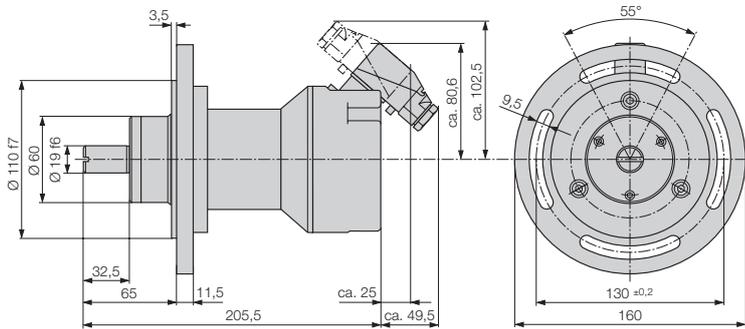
KINAX WT 707 mit Zusatzgetriebe, Steckverbinder und Flansch.
